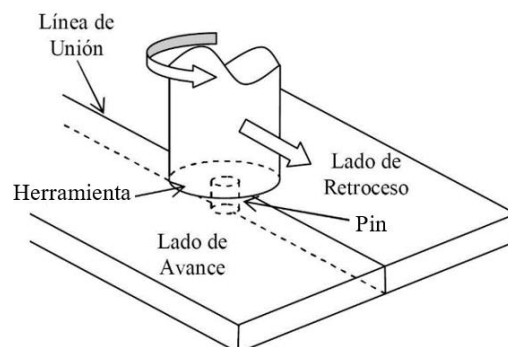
Esquema del proceso de soldadura por fricción-agitación (FSW).
